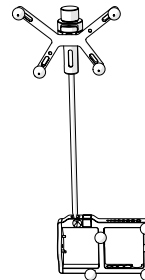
Валидационный стержень в конусе калибровочного корпуса
